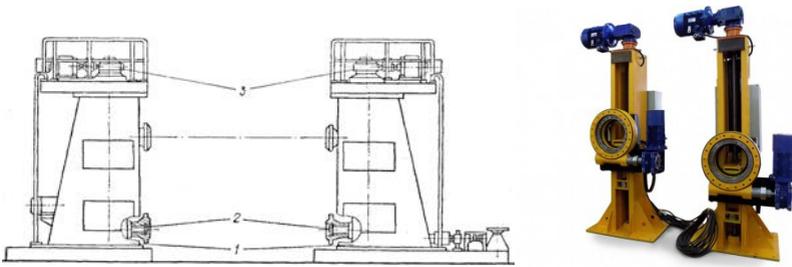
Кантователь двухстоечный с подъемными центрами:
